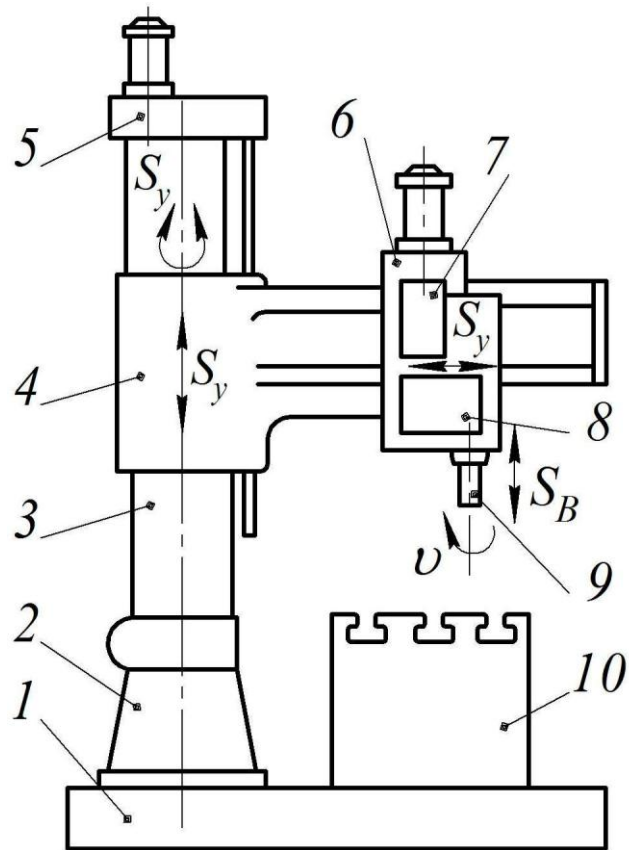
загальний вигляд радіально-свердильного верстата
